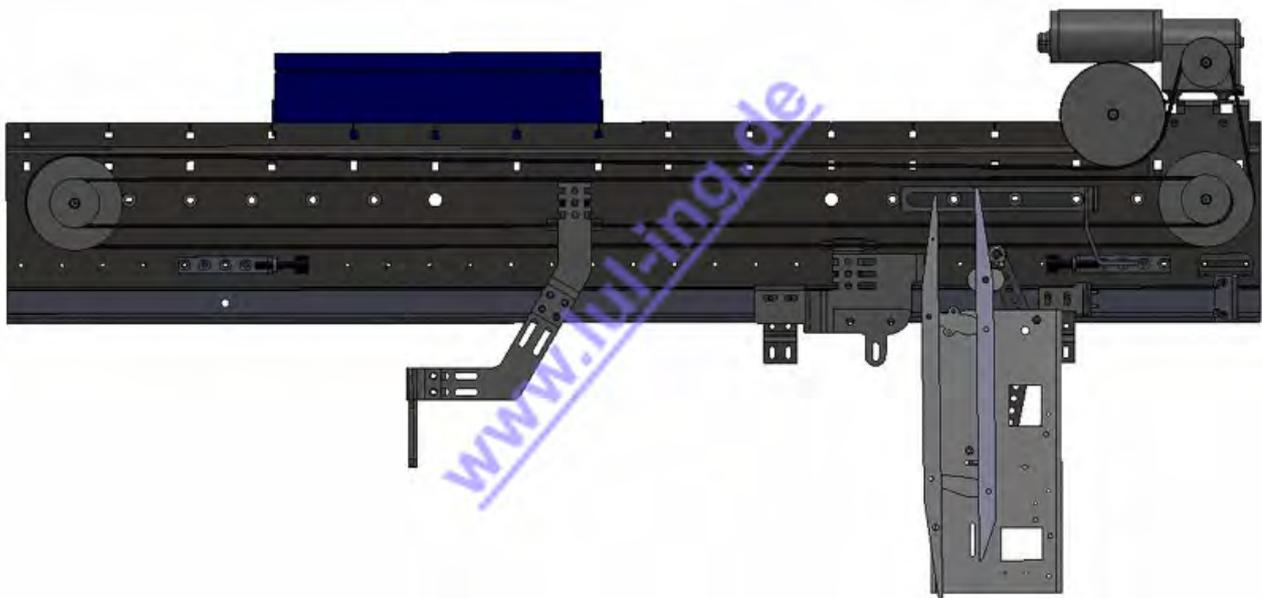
vue d'ensemble QKS8 L&L télescopique gauche
